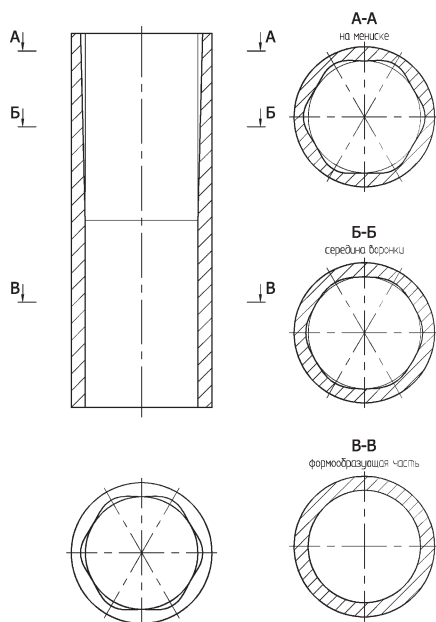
Гильза кристаллизатора конструкции «ВМ-синус» для литья круглых заготовок с шестью участками синусоидальных вогнутостей
